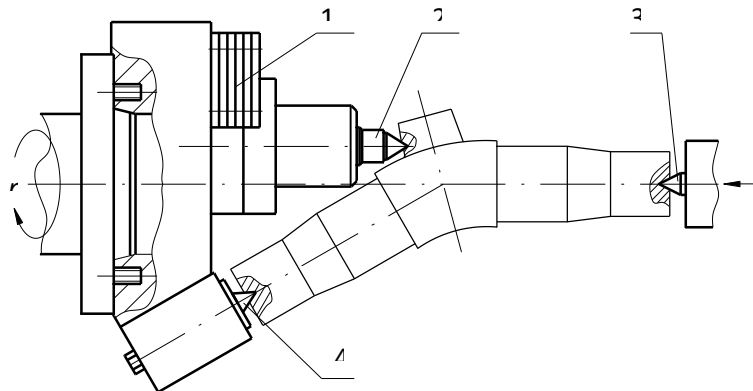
Базування й затиск криволінійної осі у пристрої токарного верстата (спосіб базування рис. 2а)
